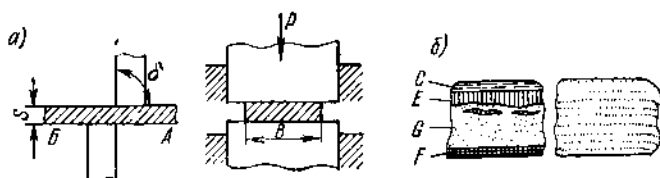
Схема резки металла ножницами с параллельными ножами и деформации металла при резке: а — схема резки; б — деформация металла при резке:
